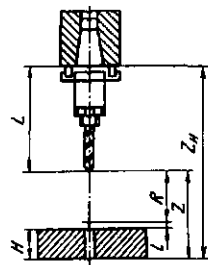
Расчетная схема определения Z_n станка с ЧПУ с вертикально расположенным шпинделем
